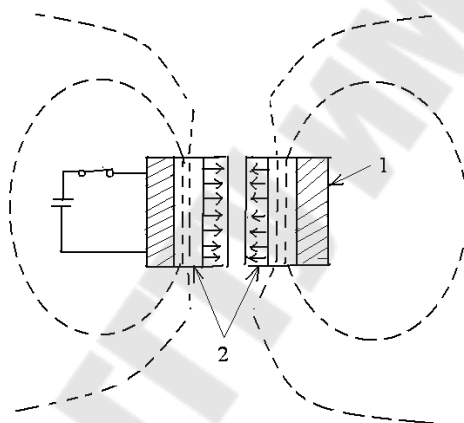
Схема магнитоимпульсной обработки: 1 – индуктор; 2 – заготовка
